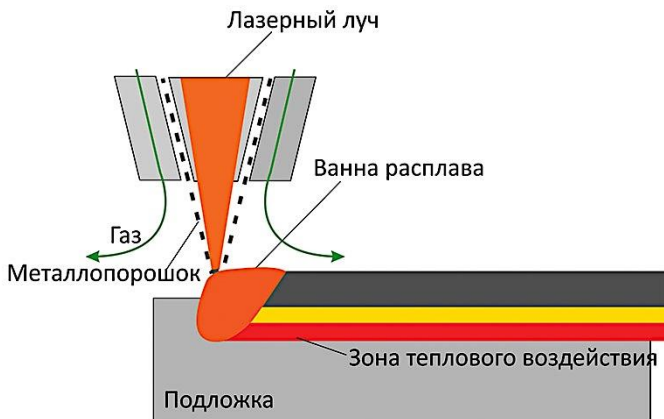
Принцип лазерной наплавки и лазерного модифицирования поверхностного слоя материала обрабатываемой детали с подачей порошкового материала в ванну расплава [206]
